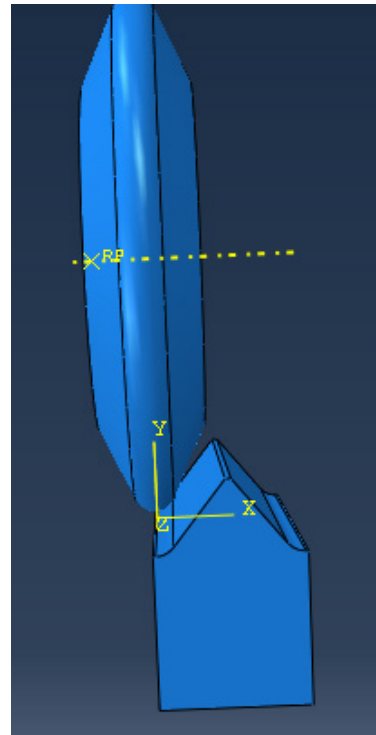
Вид с вершины оси z на модель обкатки резьбы
